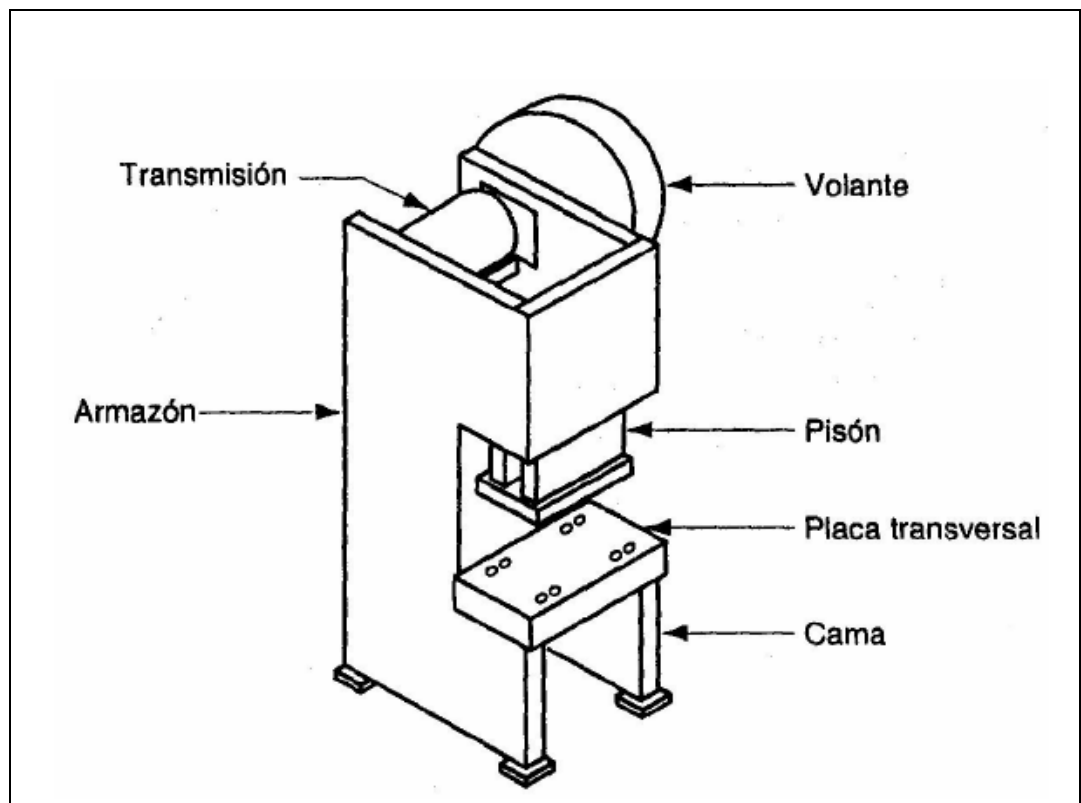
Componentes de una prensa troqueladora típica por transmisión mecánica. [6]
